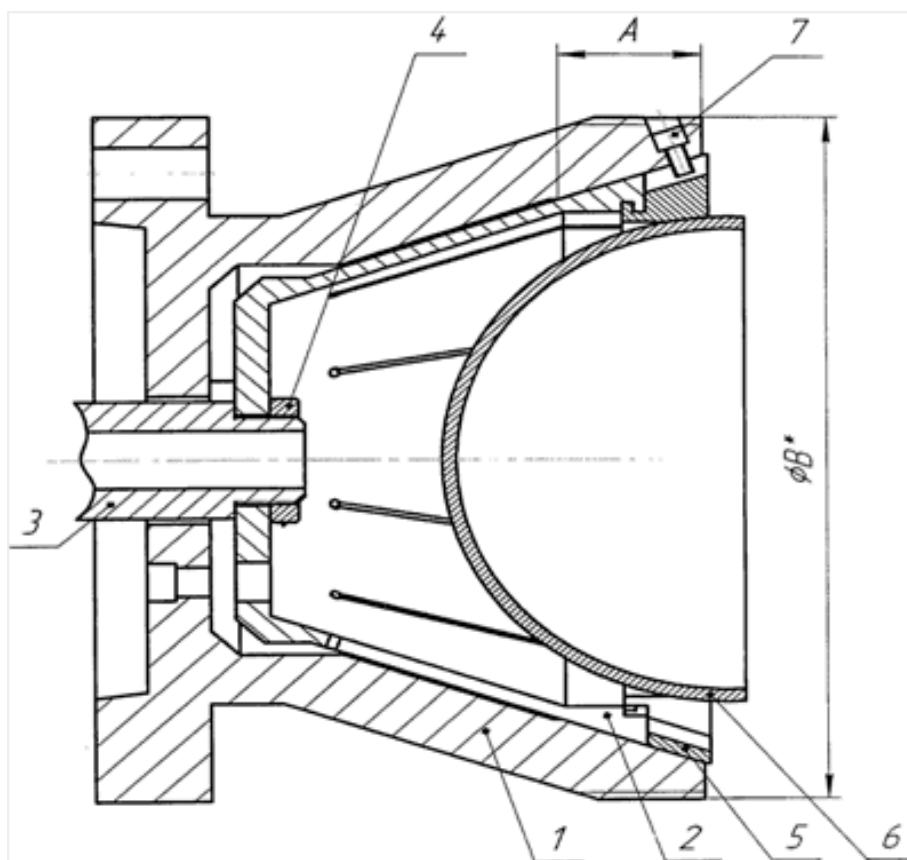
Оправка(патент РФ 2490097), разрез;
